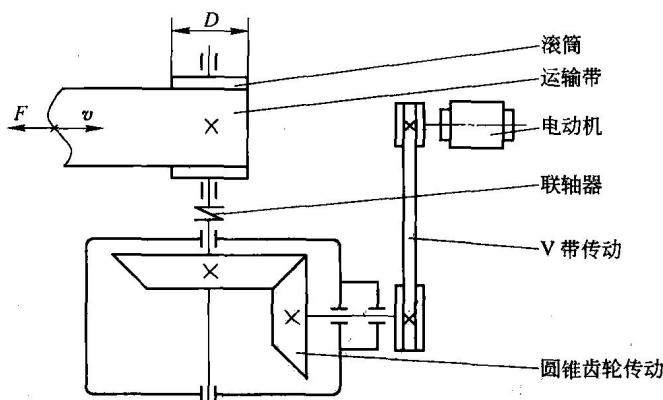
一级圆锥齿轮减速器组成的带式运输机
